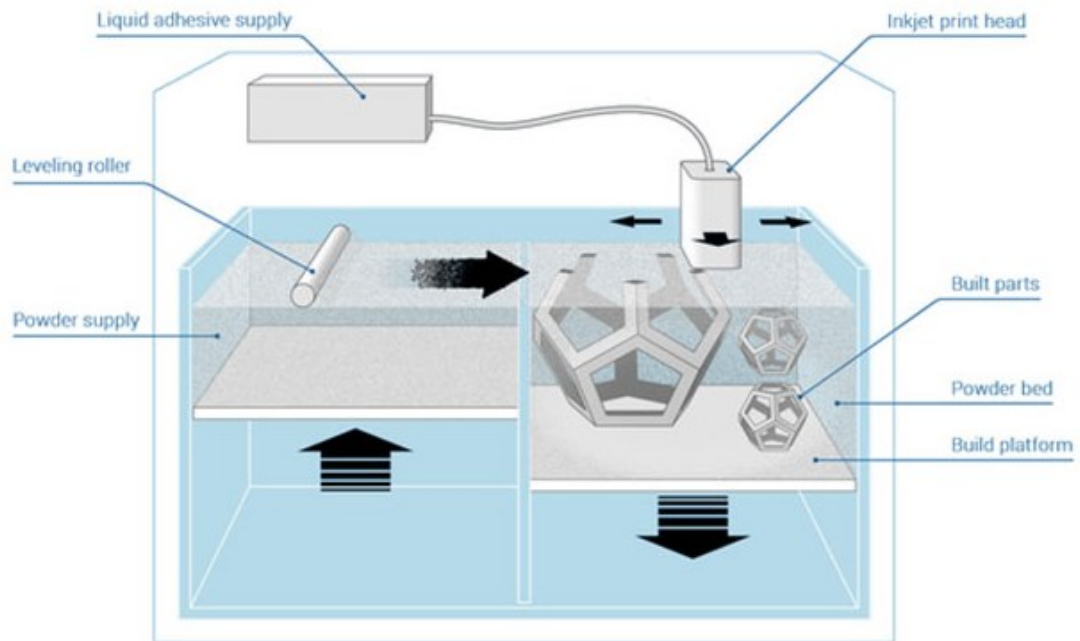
Принципова схема Binder Jetting 3D-принтеру
